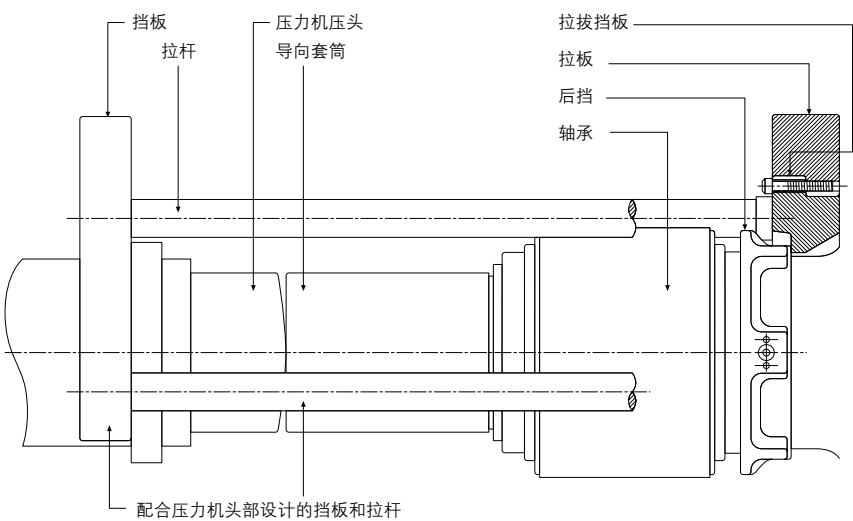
用轴承压装机或车轮压装机来拆卸轴承的装置
